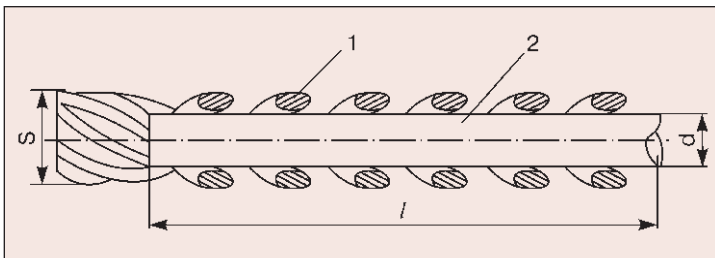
Схема сборки сварного узла перед соединением проволоки с многожильным проводом
